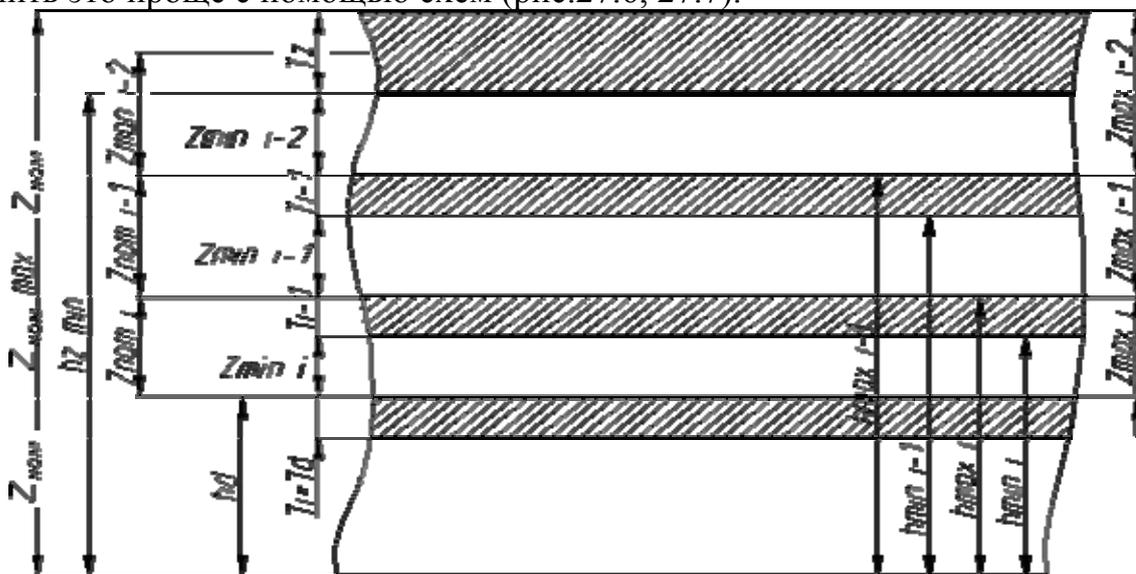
Схема связей между межпереходными размерами, припусками и допусками для охватываемых поверхностей
